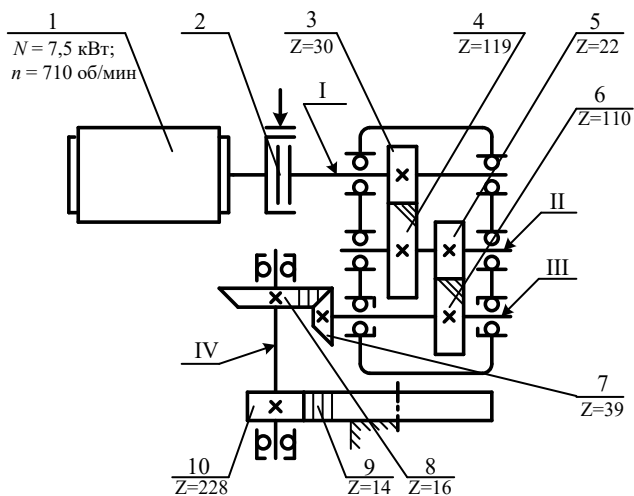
Кинематическая схема привода механизма поворота крана ДЭК-251:
